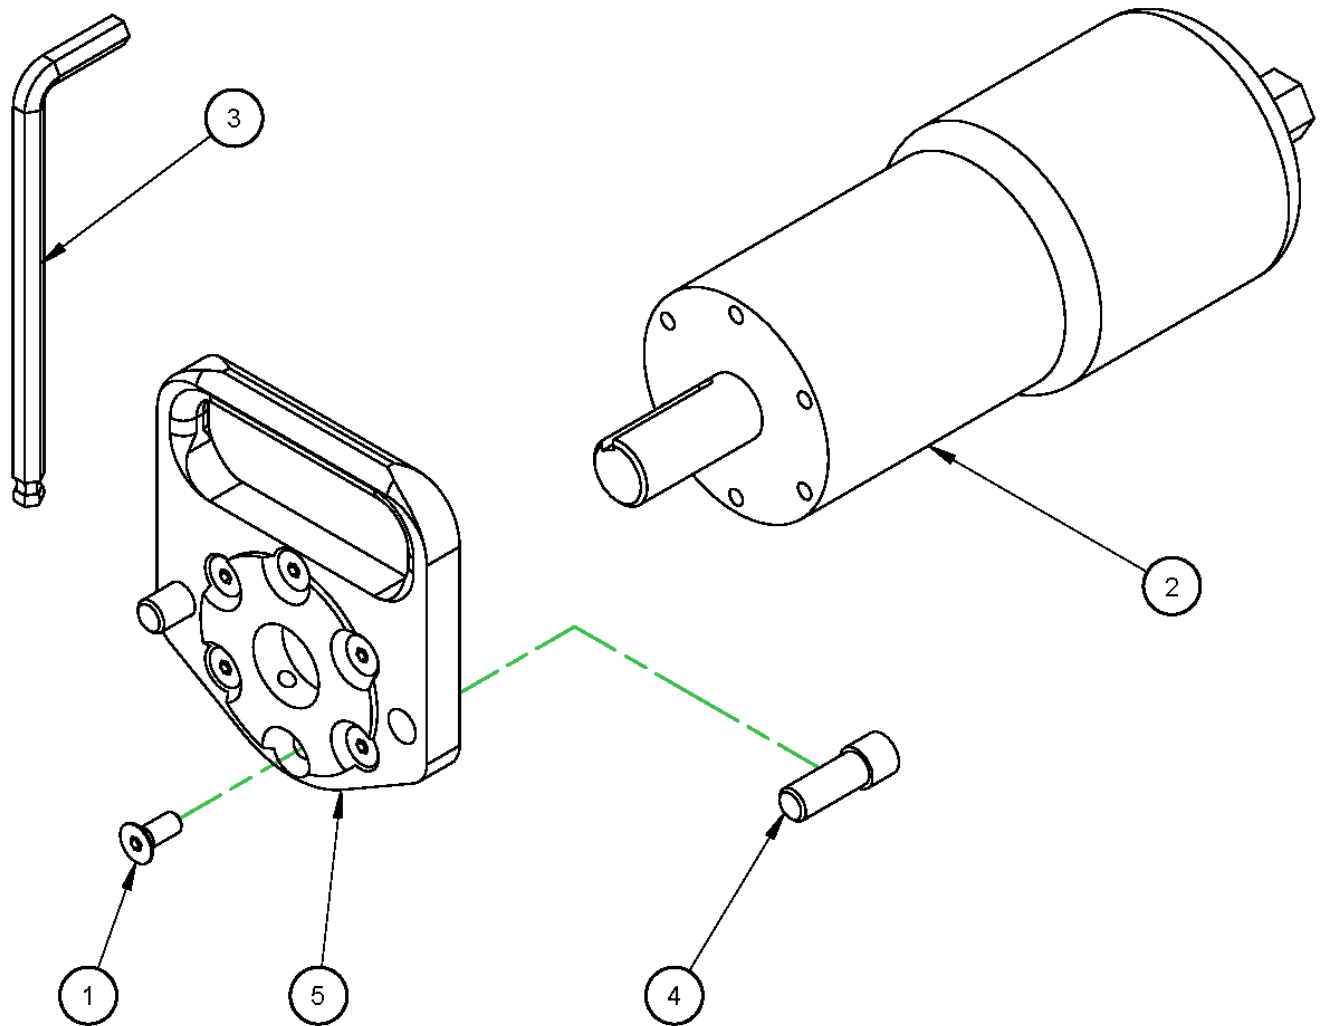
LISTE DE PIÈCES DU UNITE D'ALIMENTATION AXIALE HD (Réf 91518)
